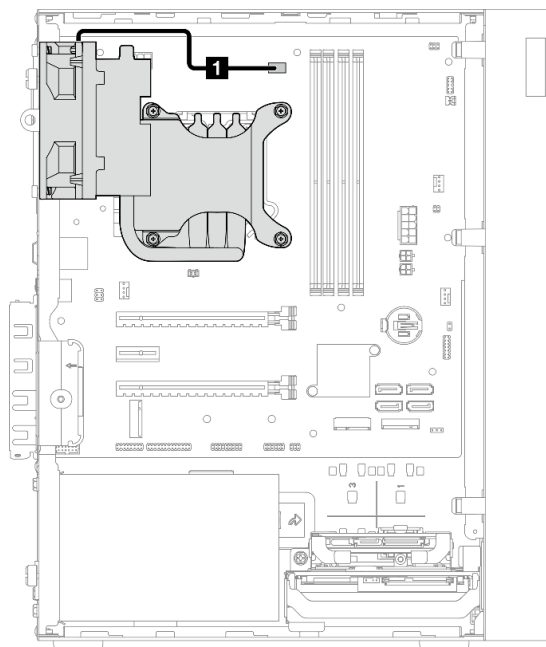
Instradamento dei cavi per il dissipatore di calore e il modulo della ventola per il processore con TDP pari a 95 W
